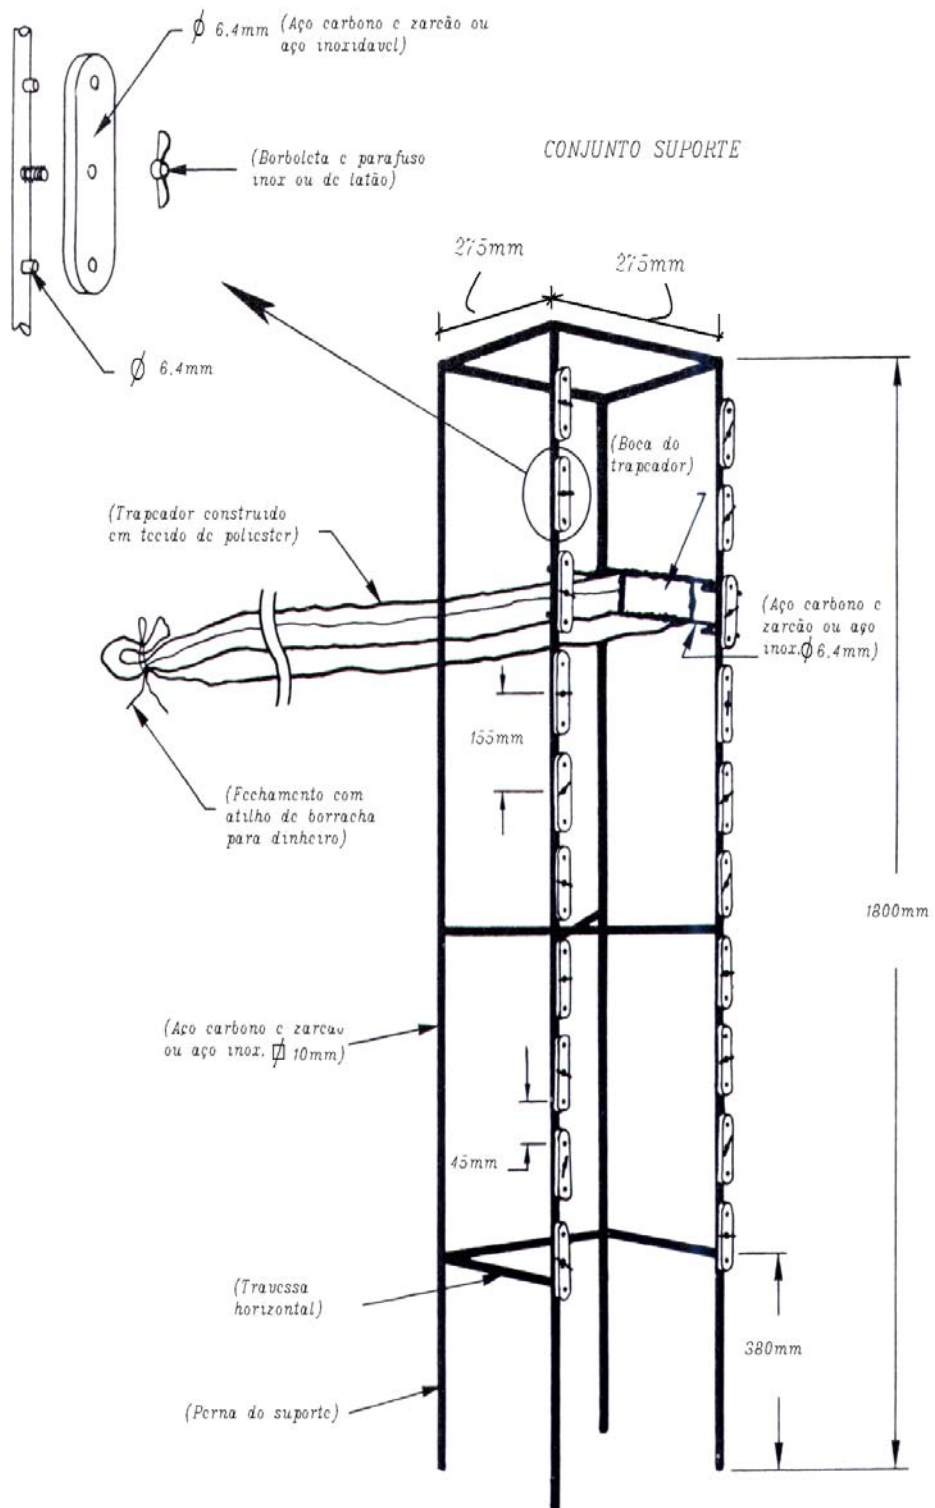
Detalhes construtivos do suporte de 'traps' (modificado de Kraus, 1987).
